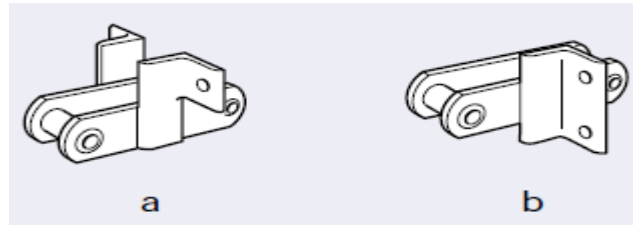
Accesorios tipo F. a) F1, accesorios soldados a placas de unión en uno o ambos lados de la cadena según sea necesario y b) F2, soldadas a placas de unión en uno o ambos lados de la cadena según sea necesario.
